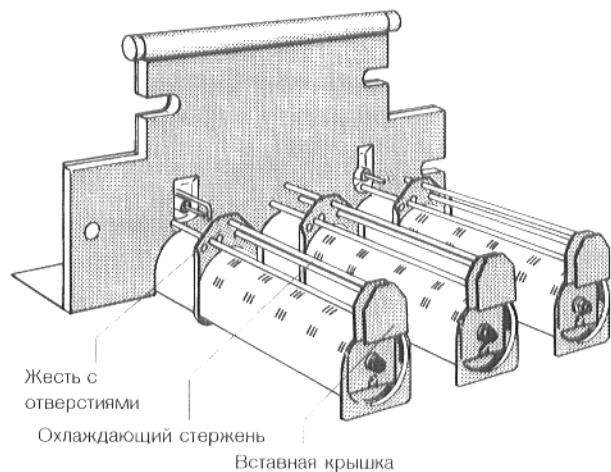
Обратная сторона щита горелки со стержнями горелки
